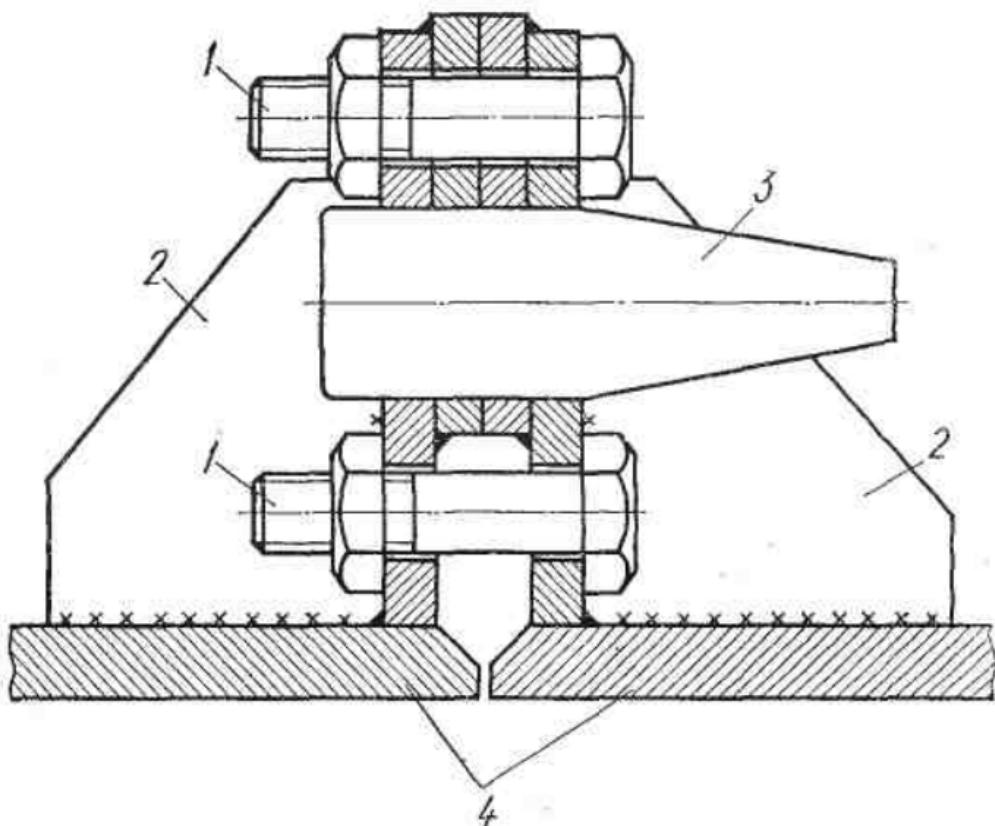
Устройство для фиксирования листов под сварку:
